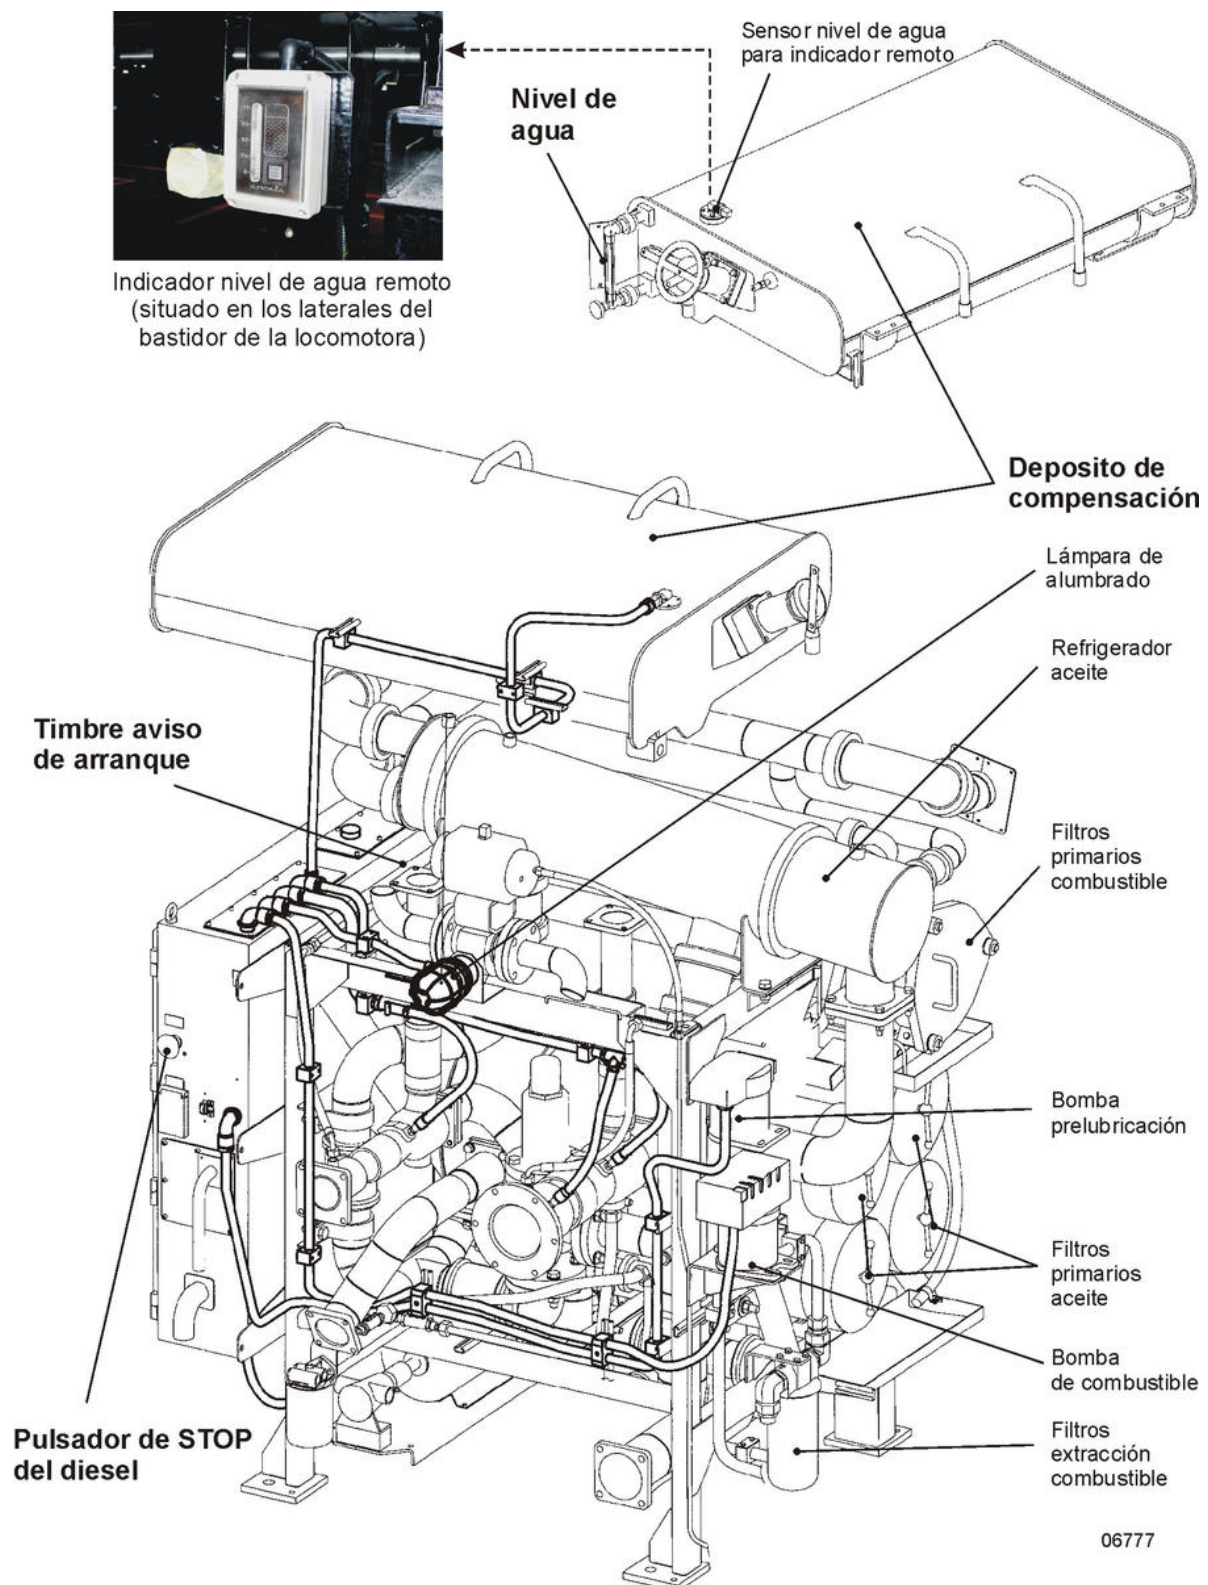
Tanque de compensación y rack de accesorios del diesel.
